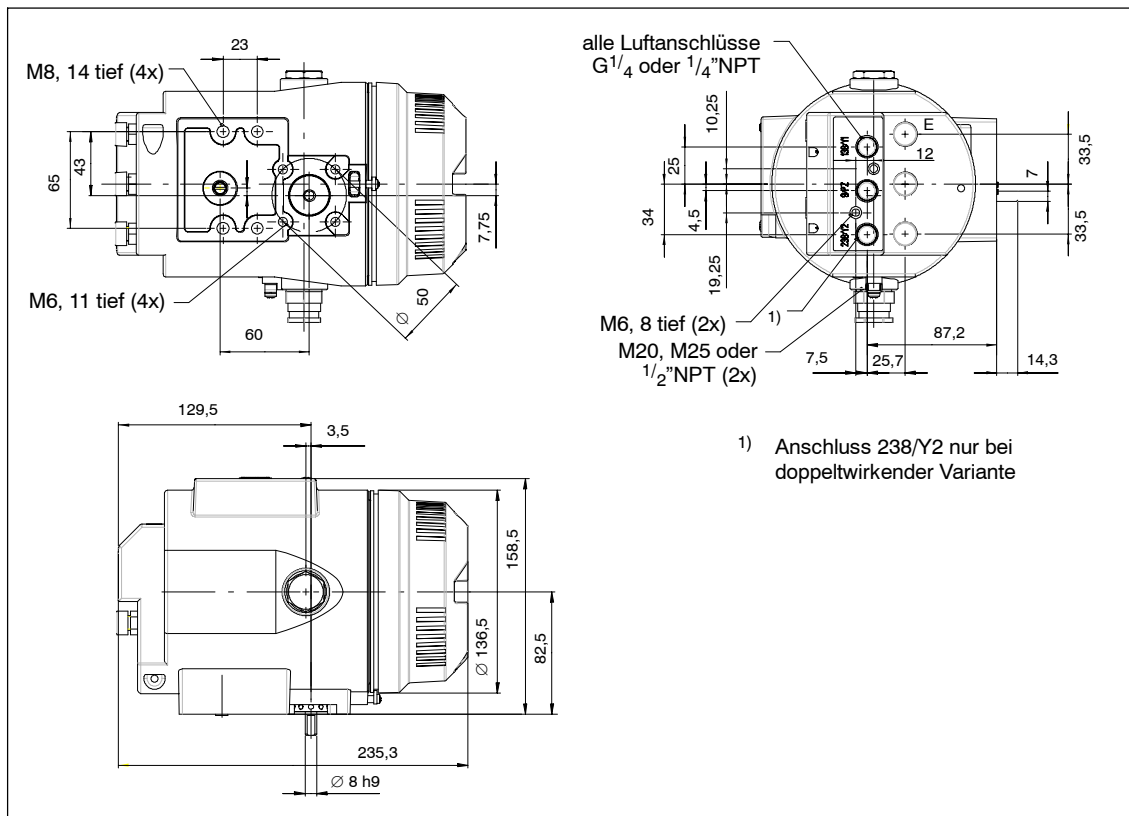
Maßbild für Stellungsregler mit Metallgehäuse in druckfestem Gehäuse 6DR5xx5
